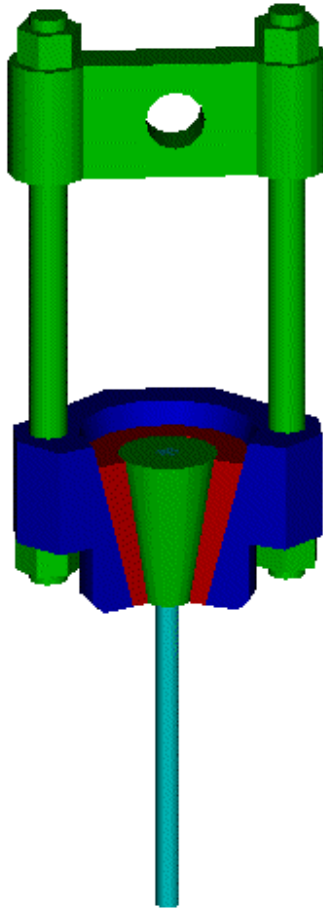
Aufnahmevorrichtung für Seile in Prüfmaschine
